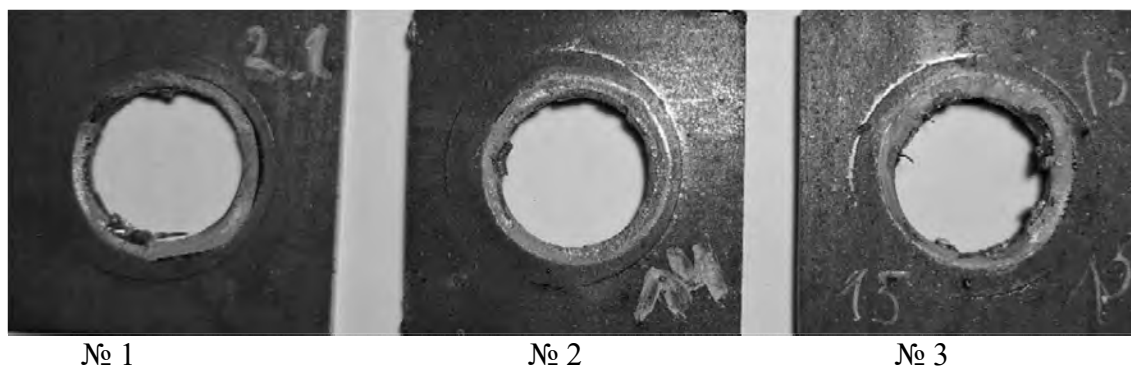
Вид области разрыва сварного соединения втулки с пластиной
